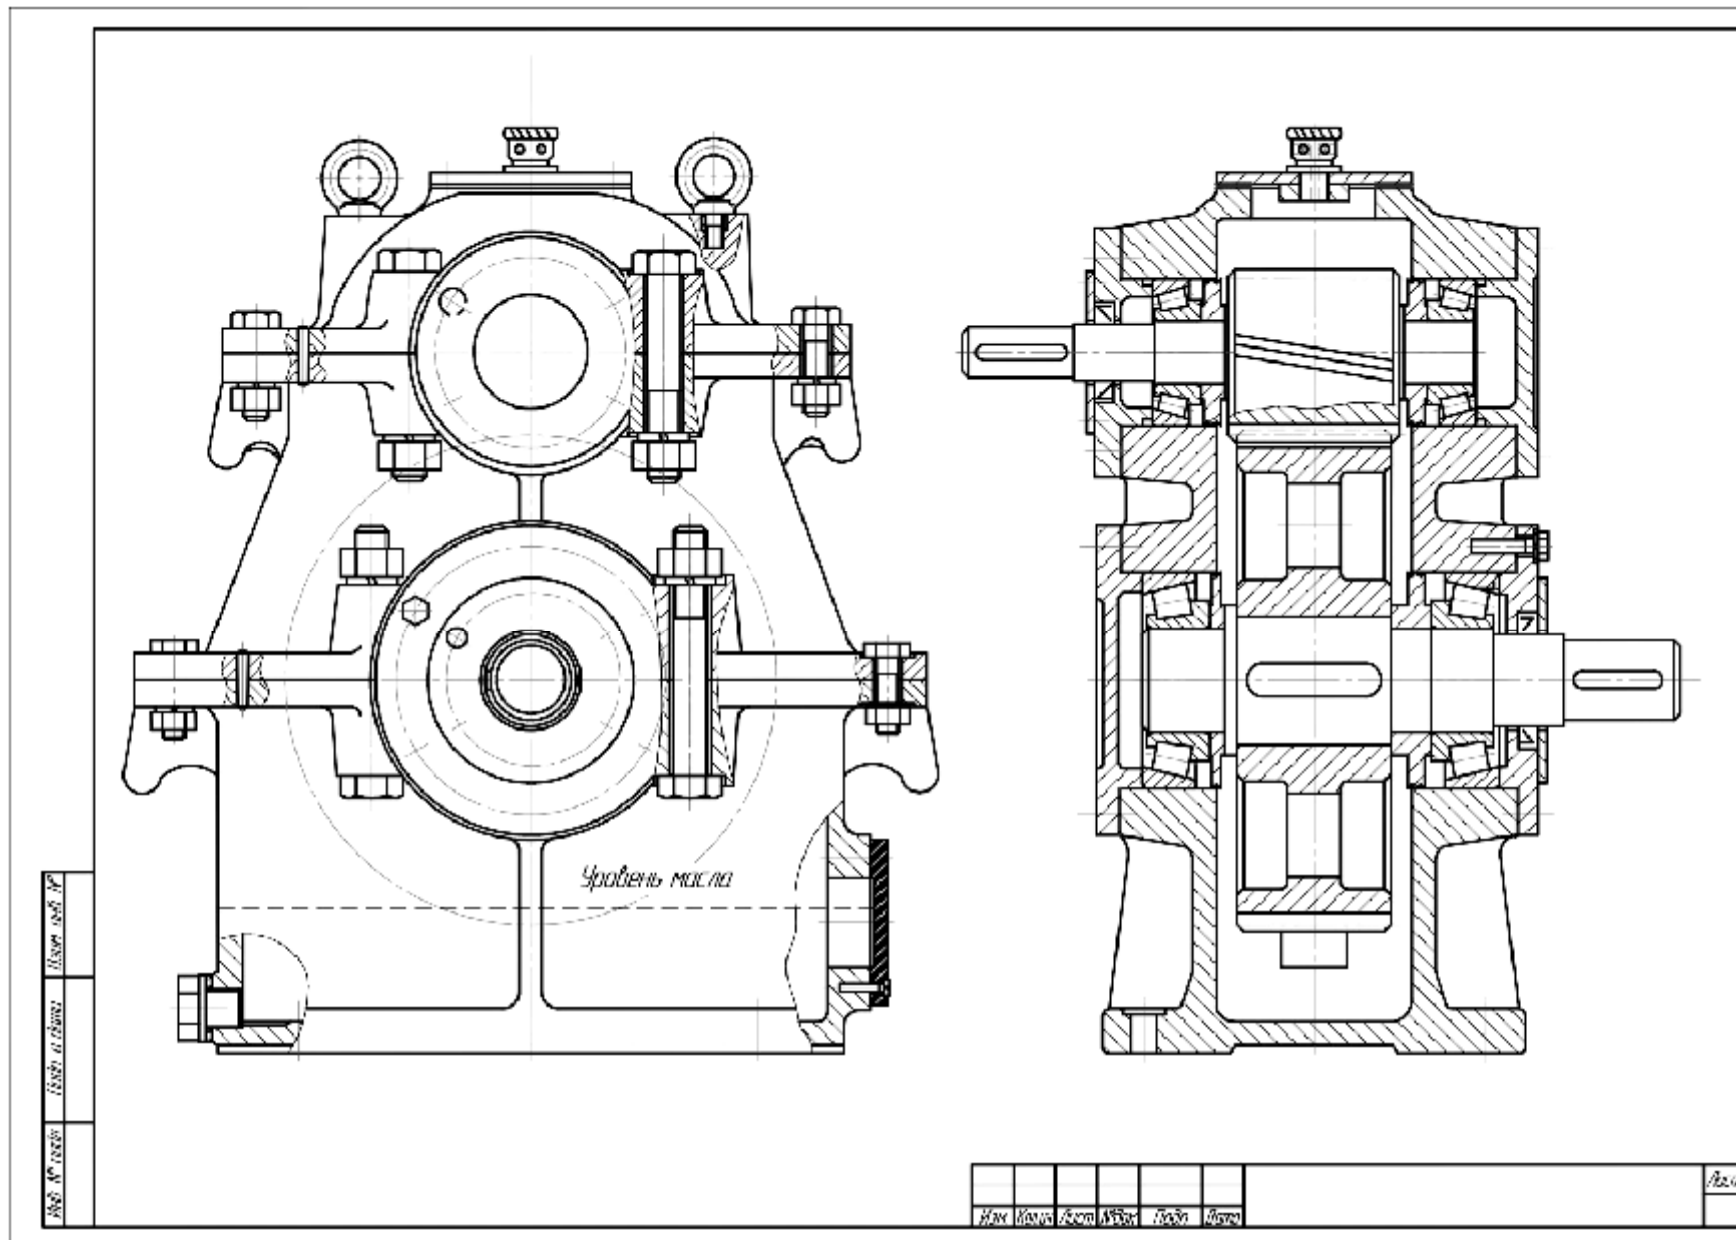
Редуктор цилиндрический одноступенчатый с верхним расположением шестерни
